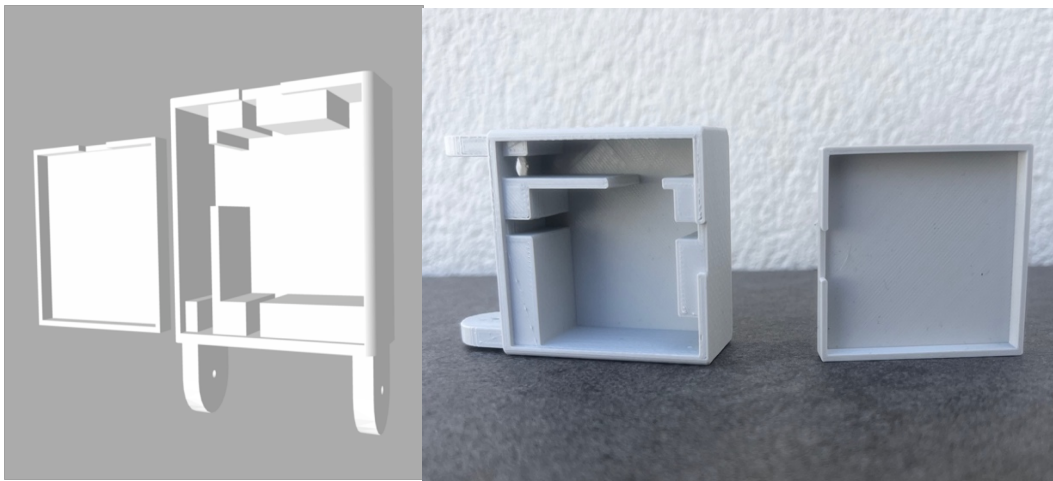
y 20. Izquierda; Vista del archivo STL proporcionado por P4H Bionics de los dedos del servo-housing. Derecha; Derecha; Resultado de la impresión del Servo-housing.
